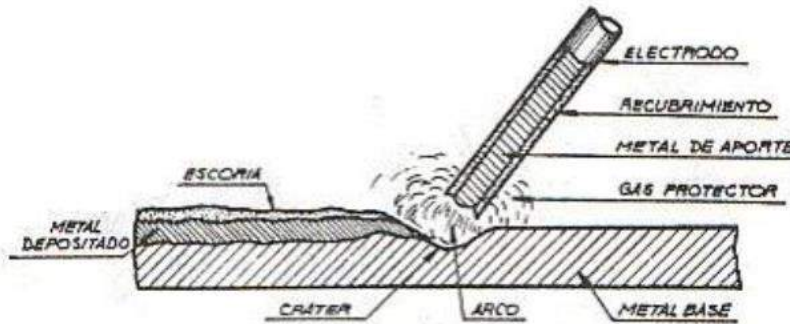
Esquema de soldadura con electrodos revestidos.
